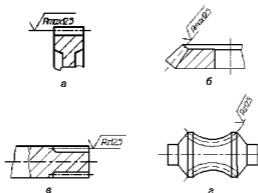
Обозначение шероховатости рабочих поверхностей зубьев: *а* – цилиндрическое колесо; *б* – коническое колесо; *в* – шлицевой вал; *г* – червяк
